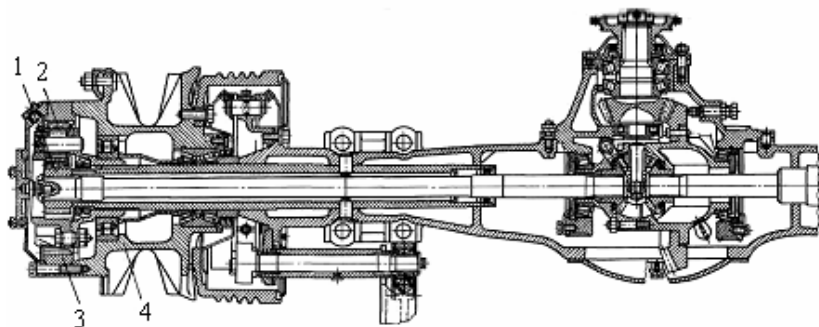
Рознесена головна передача з колісними редукторами:
